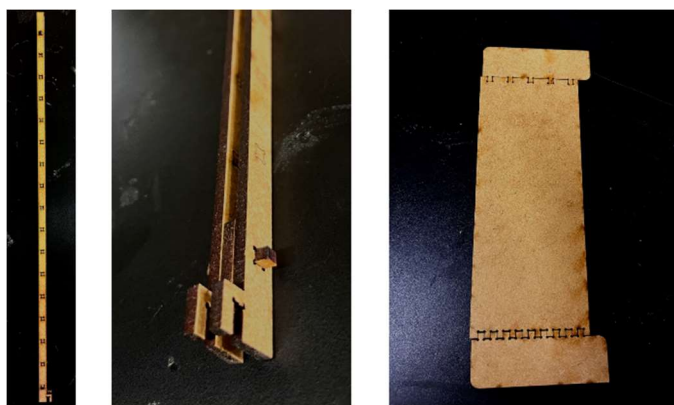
Plano de corte inicial do protótipo final na etapa 03
